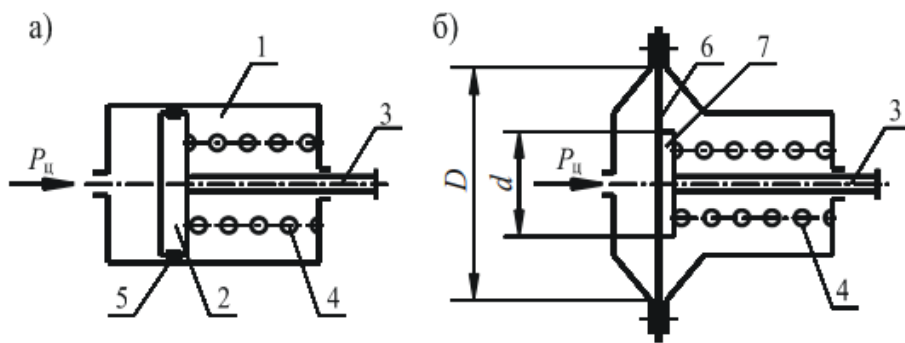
Перетворювачі пневматичного приводу:
